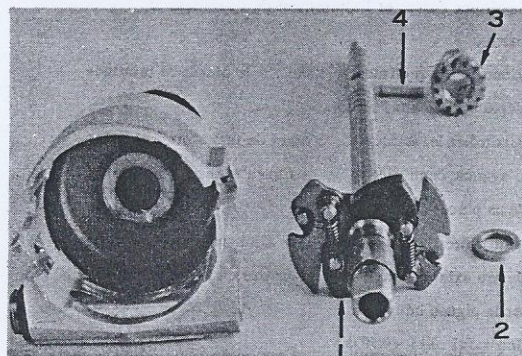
Pose de l'axe de régulateur centrifuge
